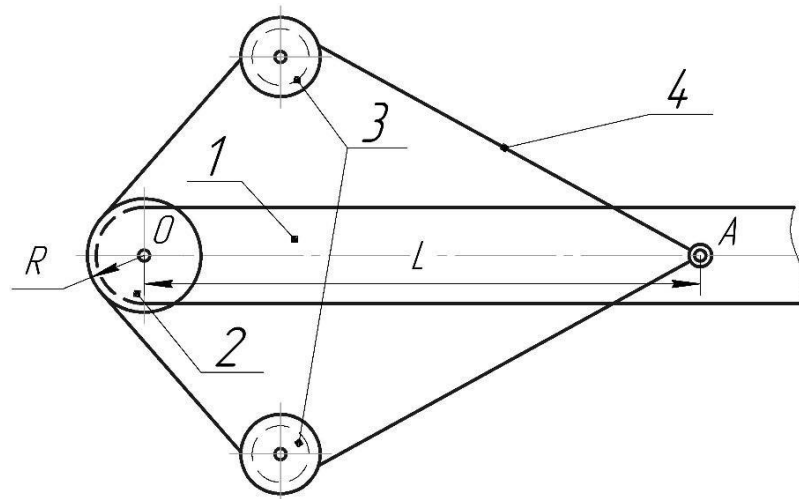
Верньєрний пристрій: 1 – повідок; 2 – шків датчика; 3 – напрямні ролики; 4 – нитка
